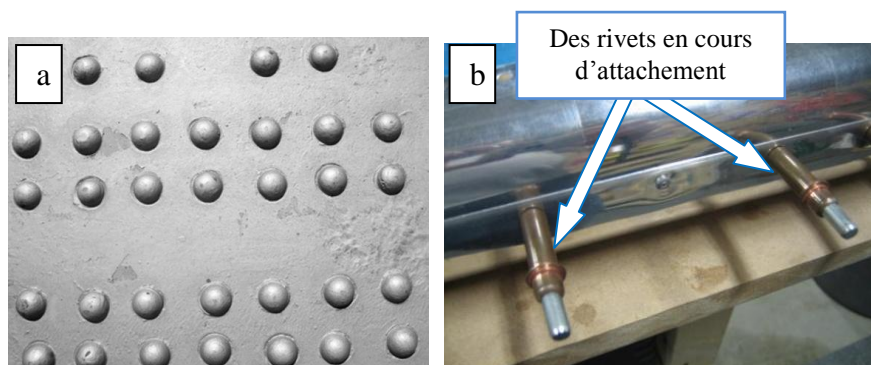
a, Des rivets attachés sur la coque d'avion, b. Rivets (AD-41-ABS) [5].
